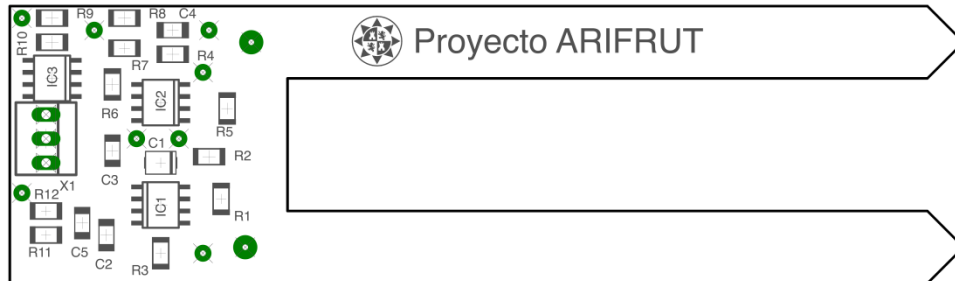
Layout del PCB del sensor experimental con distribución de los componentes electrónicos.
